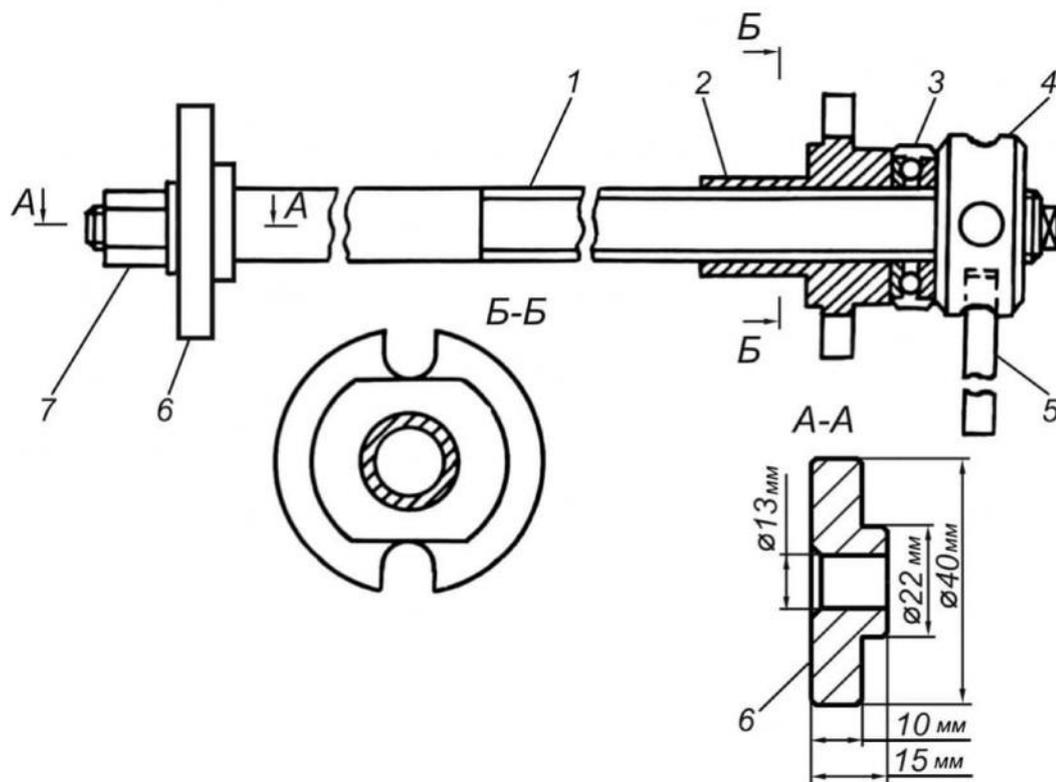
Приспособление для снятия и установки пружины: 1 - винт; 2 - опорное кольцо; 3 - подшипник; 4, 7 - гайки; 5 - вороток; 6 - шайба
